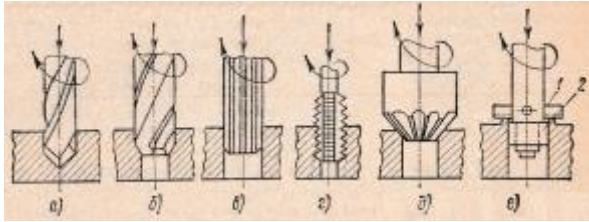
Види свердильних робіт на свердильному верстаті
